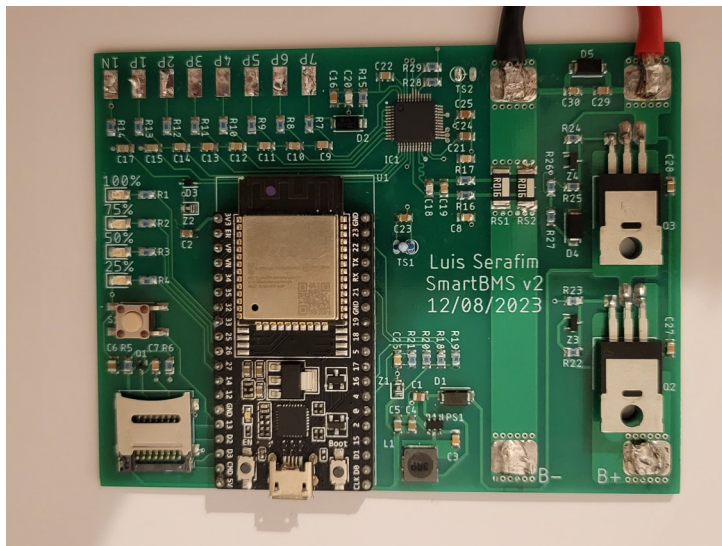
PCB do BMSiv2 com componentes soldados.
